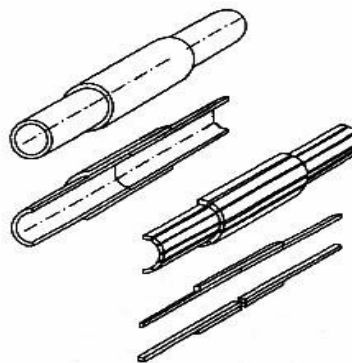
Схема подготовки образцов к различным видам испытаний
